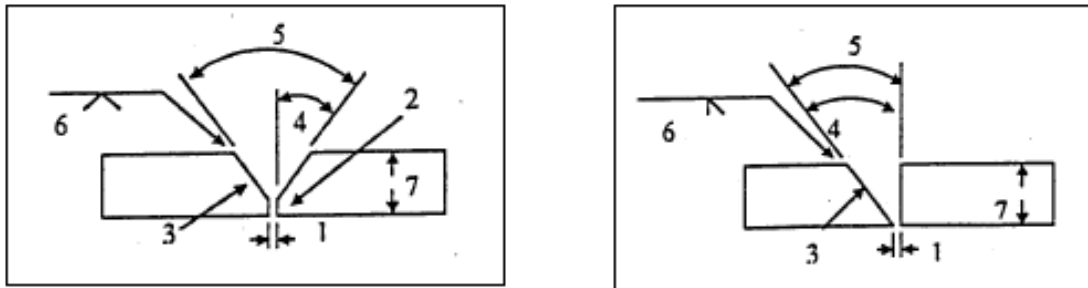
PARTES DE LAS JUNTAS A TOPE (Ref. 5)
